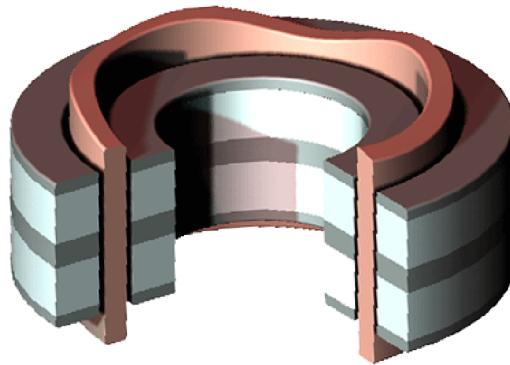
Radiální typ, vnitřní provedení [2]
